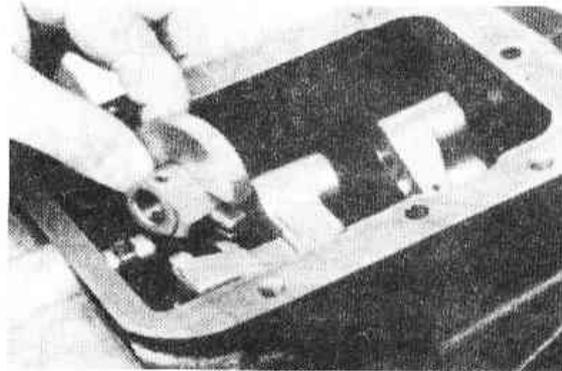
Установка рычага выбора передач и зажимной пластины коробки передач типа С (Разд.7)
